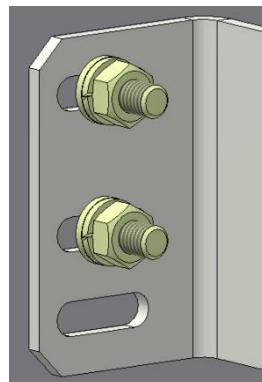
Установка блокировки в КРУ2-10 с ВМП-10К
